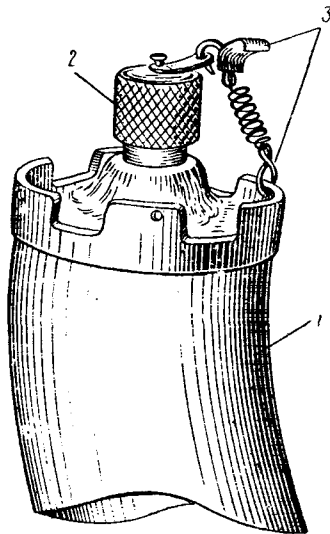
Контровка крышки заливной горловины маслосистемы редуктора и мерной линейки.
